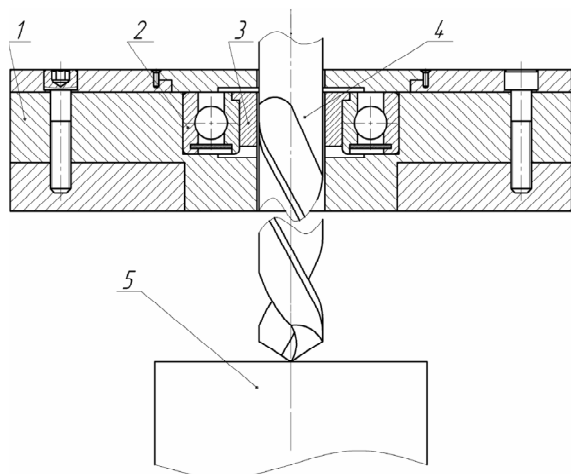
Конструкція кондуктора з обертовими втулками (пат. № 51906, Україна): 1- кондукторна плита, 2 – підшипник, 3 – обертова втулка, 4 – свердло, 5 – заготовка
